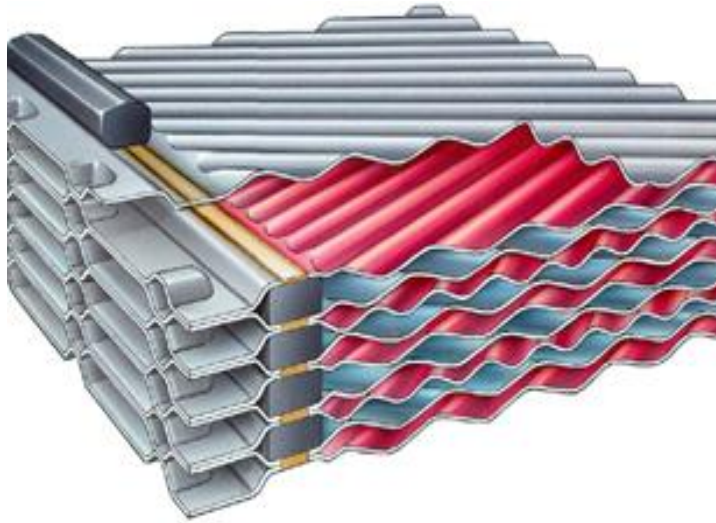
Пакет пластин теплообмінника із зварними каналами
